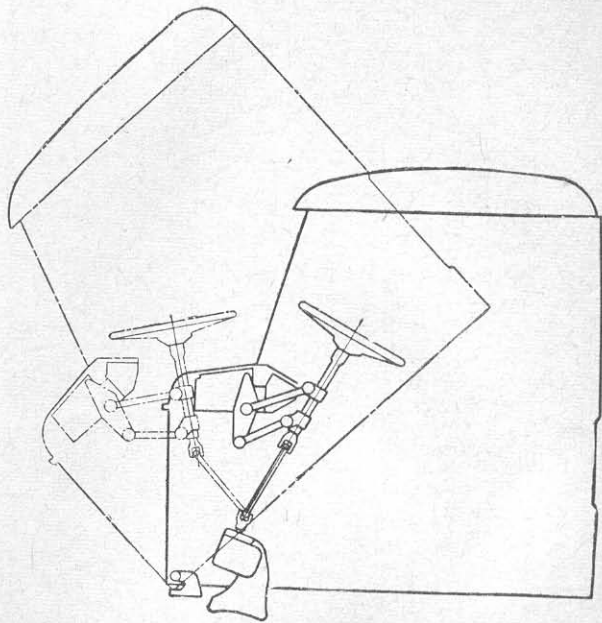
Схема изменения положения рулевого вала при откидывании кабины
